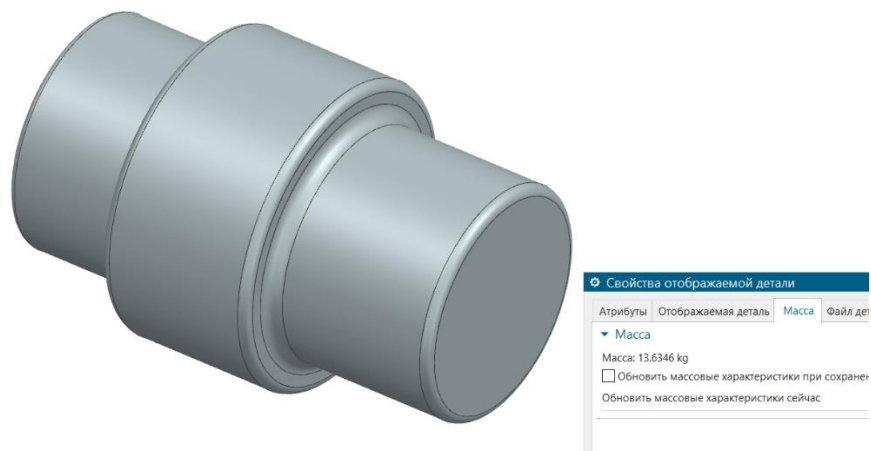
3Д-модель заготовки отриманої на молоті
